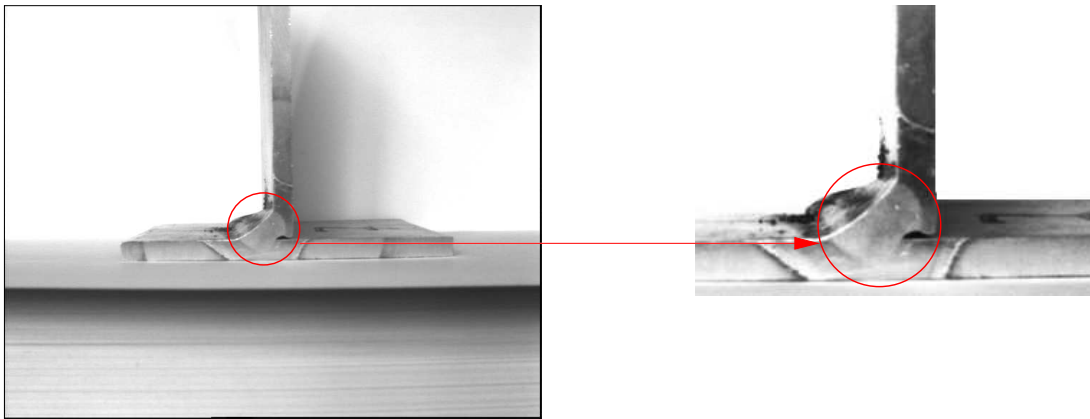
Ein aufgeschnittener Aluminium-Testkörper (Länge der Seitenteile ca. 6 cm). Die Tiefe der hier sichtbaren Verschweißung (heller Bereich innerhalb des Kreises) soll im CT-Bild ermittelt werden.
